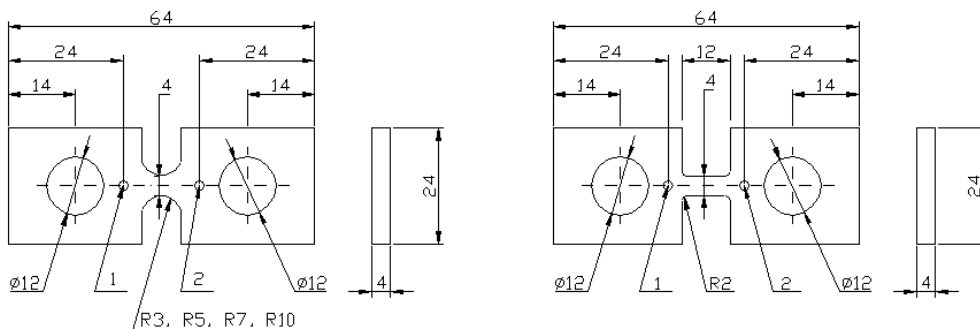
Размеры образцов и схема расположения преобразователей АЭ:
